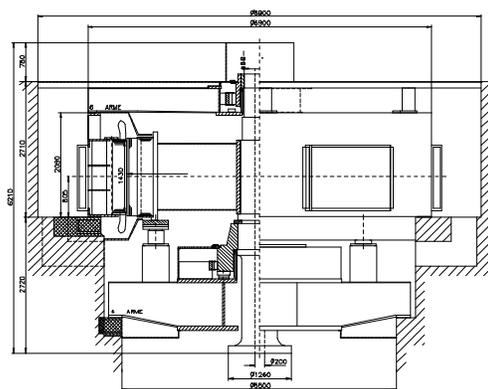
DIMENSIONAL COM MANCAL PTFE
